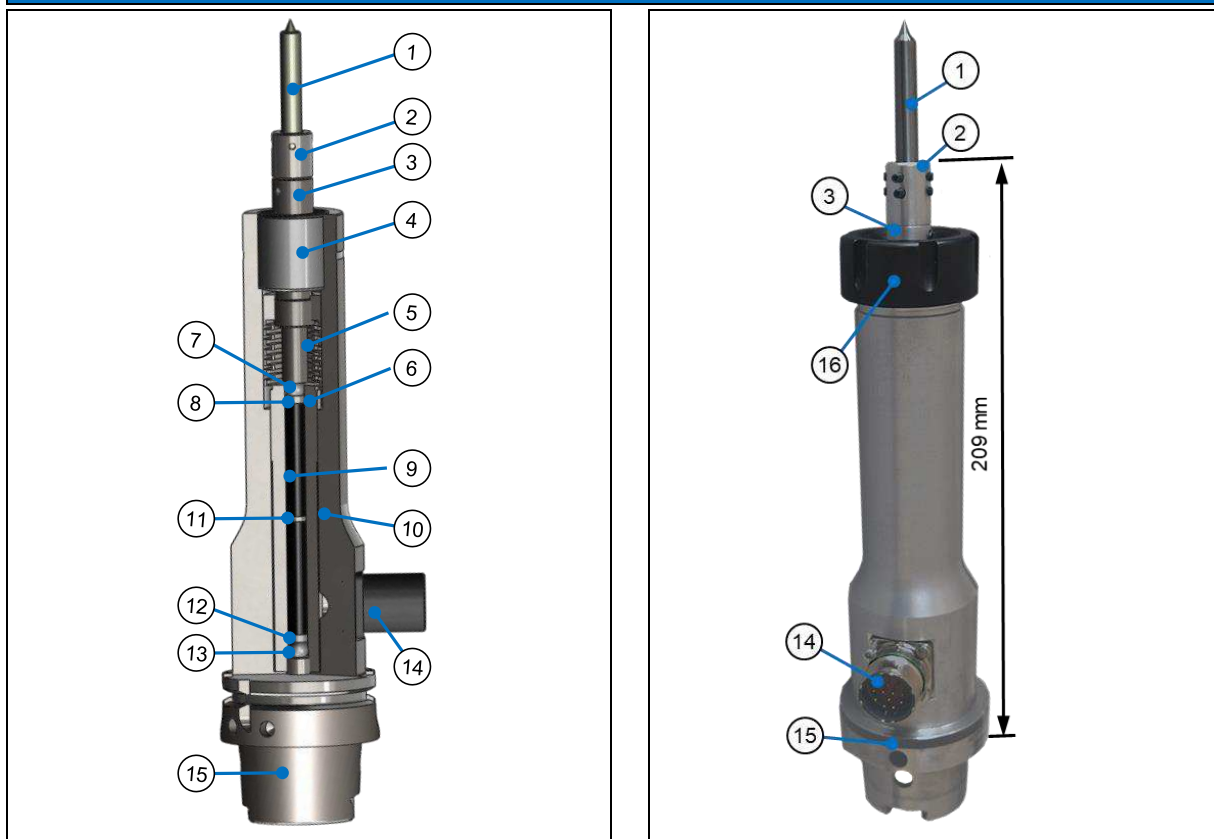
MHP-PZ-Aktor: links Teilschnittdarstellung im CAD, rechts: gefertigter Aktor in der Ausführung mit HSK-63 Schnittstelle; (1) Werkzeug; (2) Einstellbuchse; (3) Aufnahme; (4) Lager; (5) Lagerbalg; (6) Aufnahme; (7) Kugel; (8) Scheibe; (9) Piezo; (10) Gehäuse; (11) Scheibe; (12) Scheibe, (13) Kugel; (14) Anschluss; (15) HSK 63
